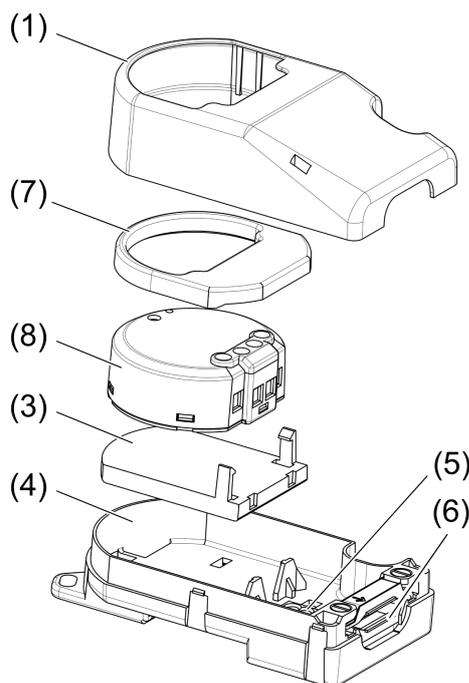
Komponenten Einbaugehäuse mit Dimmer Mini
